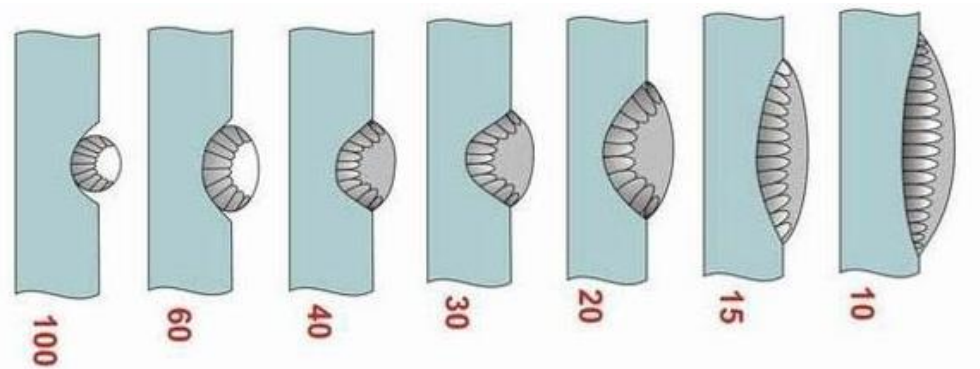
Швидкість зварювання і вид шва, м/ч.
